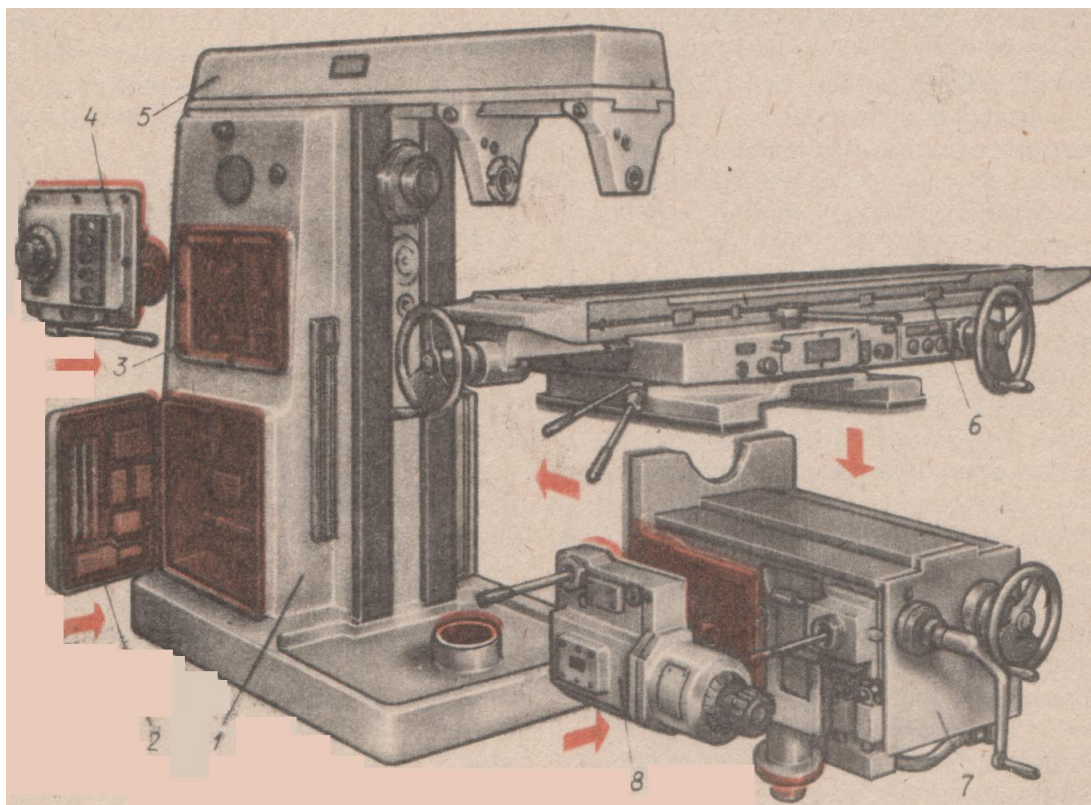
Основные части консольного горизонтально-фрезерного станка
